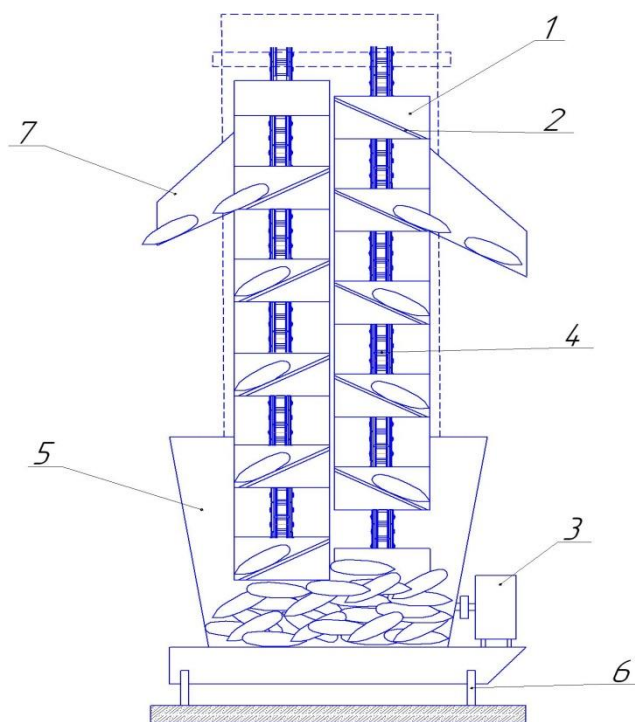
Элеваторное ориентирующее устройство: 1 - основная ориентирующая поверхность; 2- вспомогательная ориентирующая поверхность; 3- мотор-редуктор; 4- приводная цепь; 5- загрузочный бункер; 6- опорные колеса; 7- выгрузной лоток.
